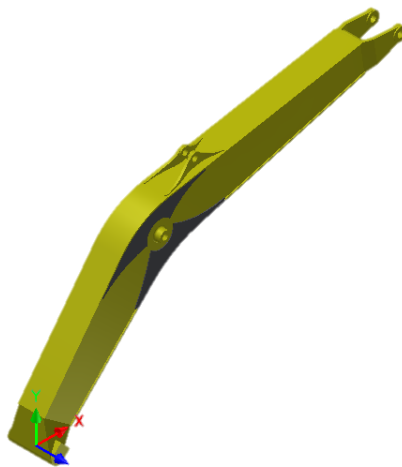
Pandangan Depan Boom Excavator Kelas 20 Ton Unreinforcement
